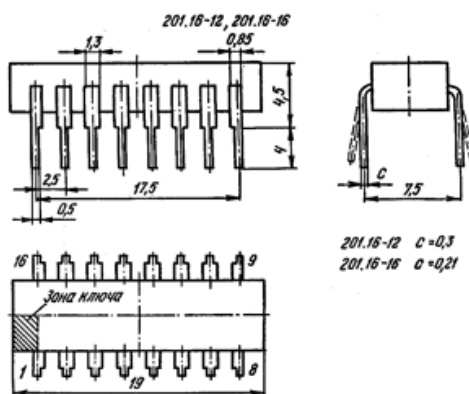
Габаритні розміри мікросхеми LS7232
